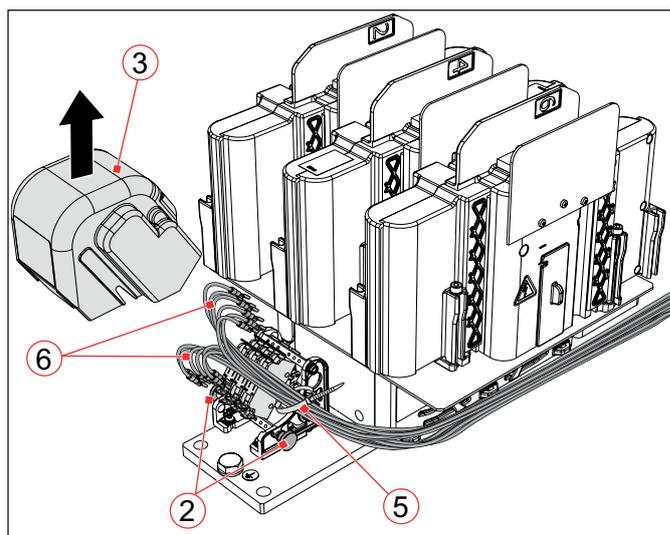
CA 1315/CA 1330: Hilfsschalter anschließen, Beispiel für Flachsteckeranschluss
